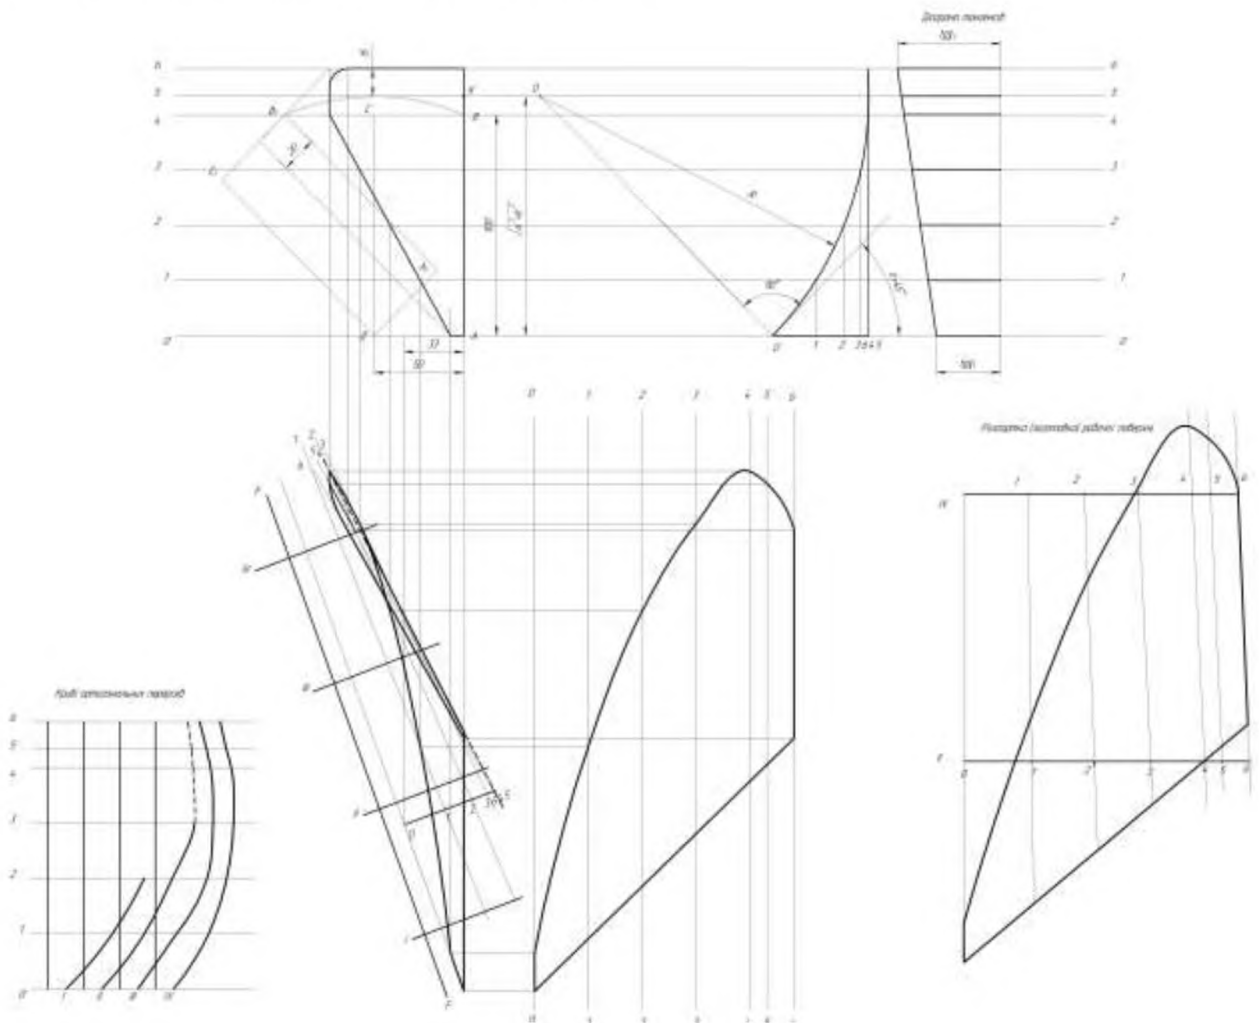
Результати побудови проєкцій полиці та заготовки для її виготовлення
